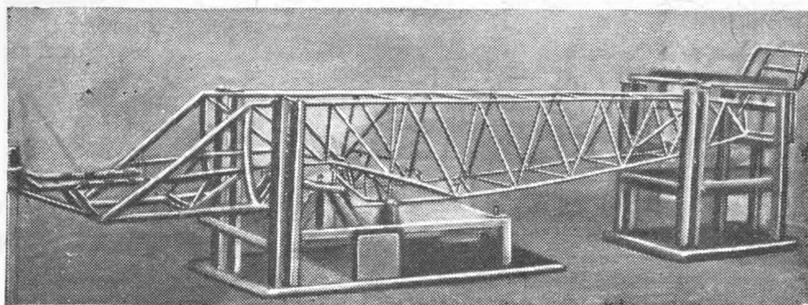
Стапель для сборки и сварки панелей фюзеляжа.
